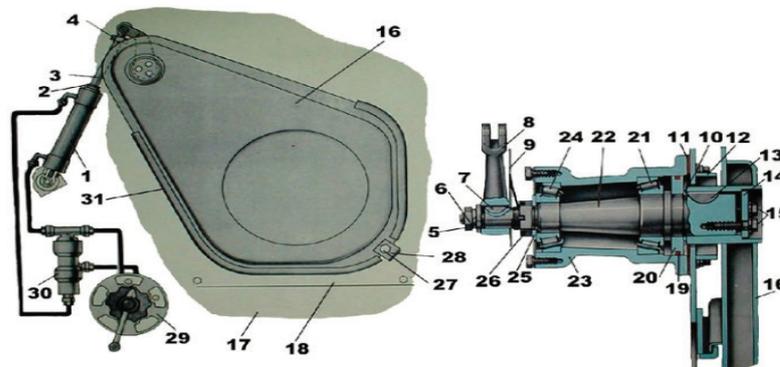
Заслонка водомета: 1-гидроцилиндр; 2 и 10 — регулировочные шайбы; 3 — шток цилиндра; 4 — контргайка; 5 — гайка крепления рычага; 6,14 и 25 шайбы; 7 и 13 — шпонки; 8 — рычаг валика заслонки; 9 — рычаг включения сигнализации; 11 — уплотнительная прокладка; 12 — упорное кольцо; 15 — болты крепления заслонки; 16 — заслонка; 17 и 18 — листы кормы; 19 — уплотнительное кольцо; 20 — фланец; 21 и 24 — роликовые подшипники; 22 — валик заслонки; 23 — опора; 26 — гайка; 27 — упор; 28 — упорный штифт; 29 — гидрораспределительный аппарат; 30 — гидрозамок; 31 — лабиринт
